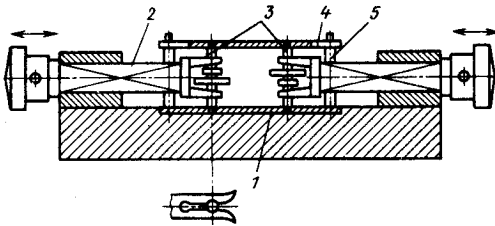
Приспособление для сборки зубчатого механизма прибора
